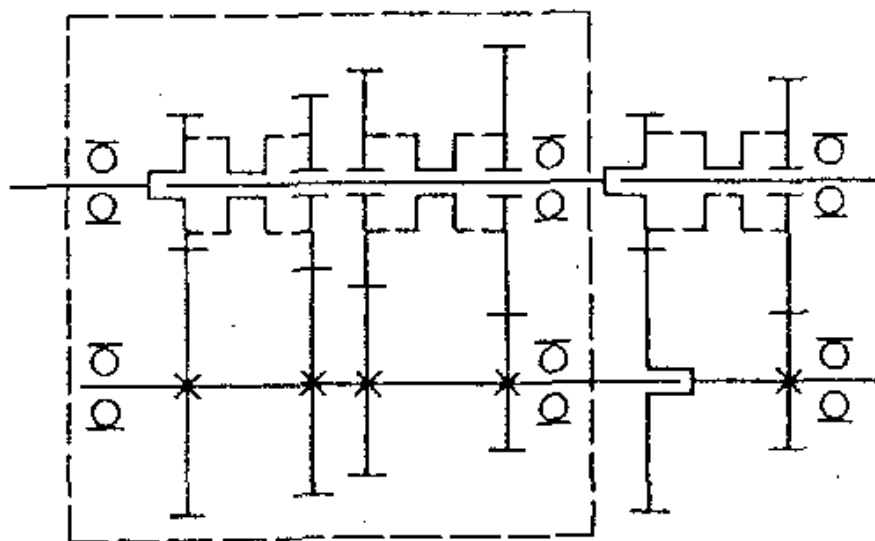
Кинематическая схема 4-х ступенчатой коробки передач и 2-х ступенчатого диапазонного делителя
